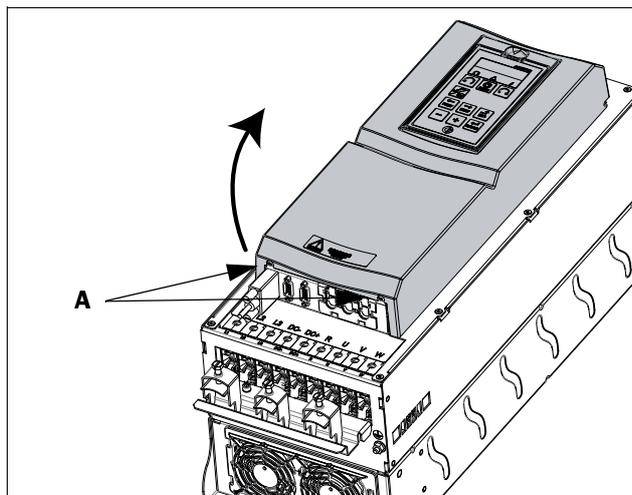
Снятие передней крышки на типоразмере C2-F2 и FA2 (общая схема)
